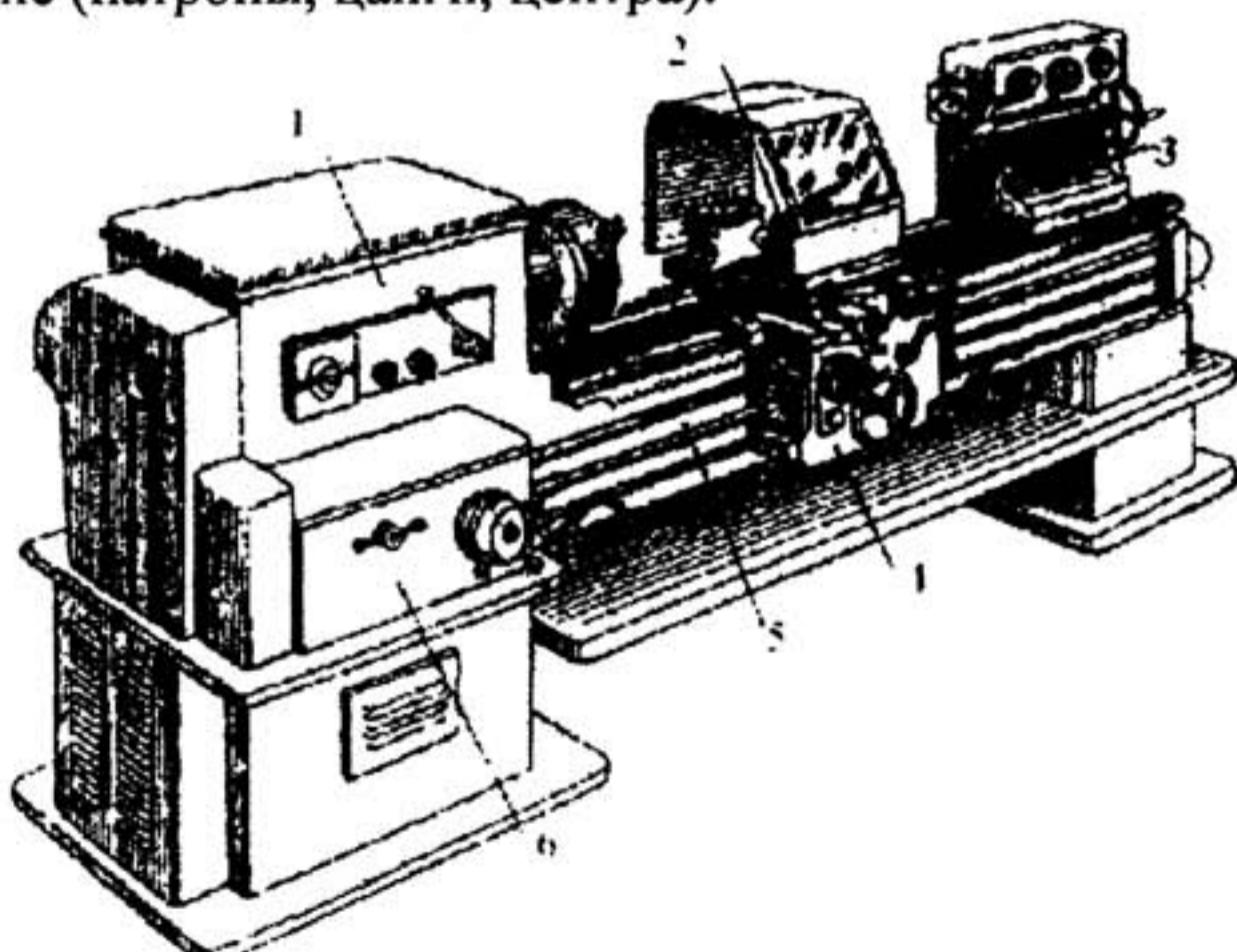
Токарно-винторезный станок мод. 16К20.
